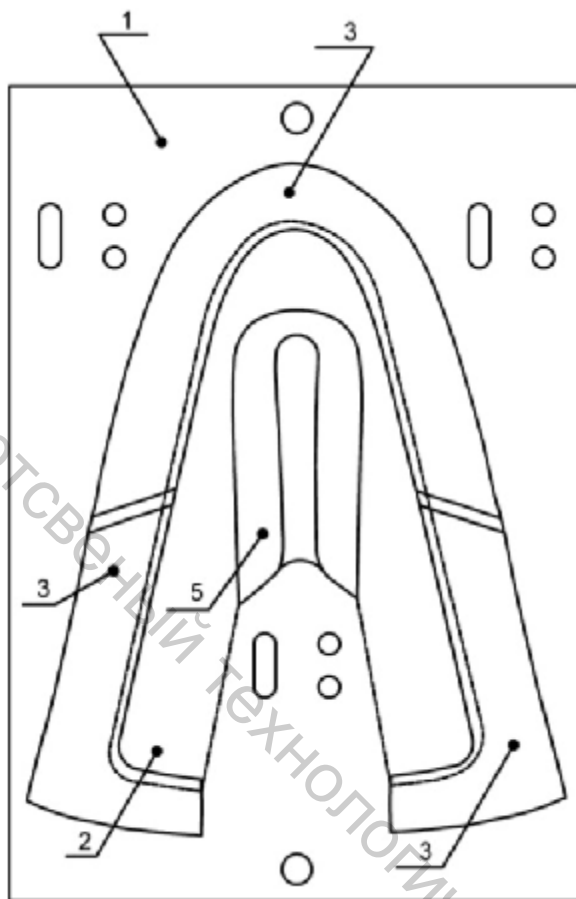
Кассета с установленными на ней деталями заготовки верха обуви
